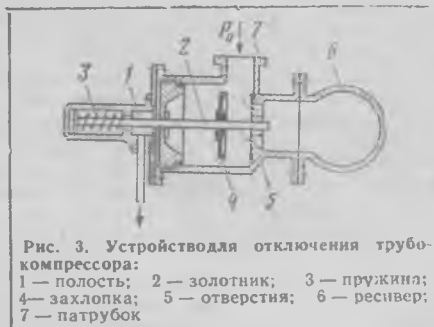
Устройство для отключения турбокомпрессора: 1 — полость; 2 — золотник; 3 — пружина; 4 — захлопка; 5 — отверстия; 6 — ресивер; 7 — патрубок
